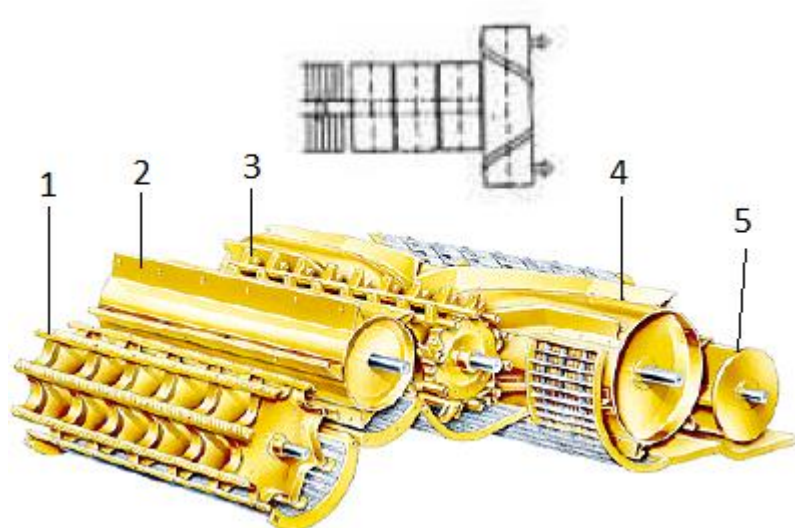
Rotační separátor: 1- rotor, 2- plášť rotoru, 3- zakřivené lopatky.
